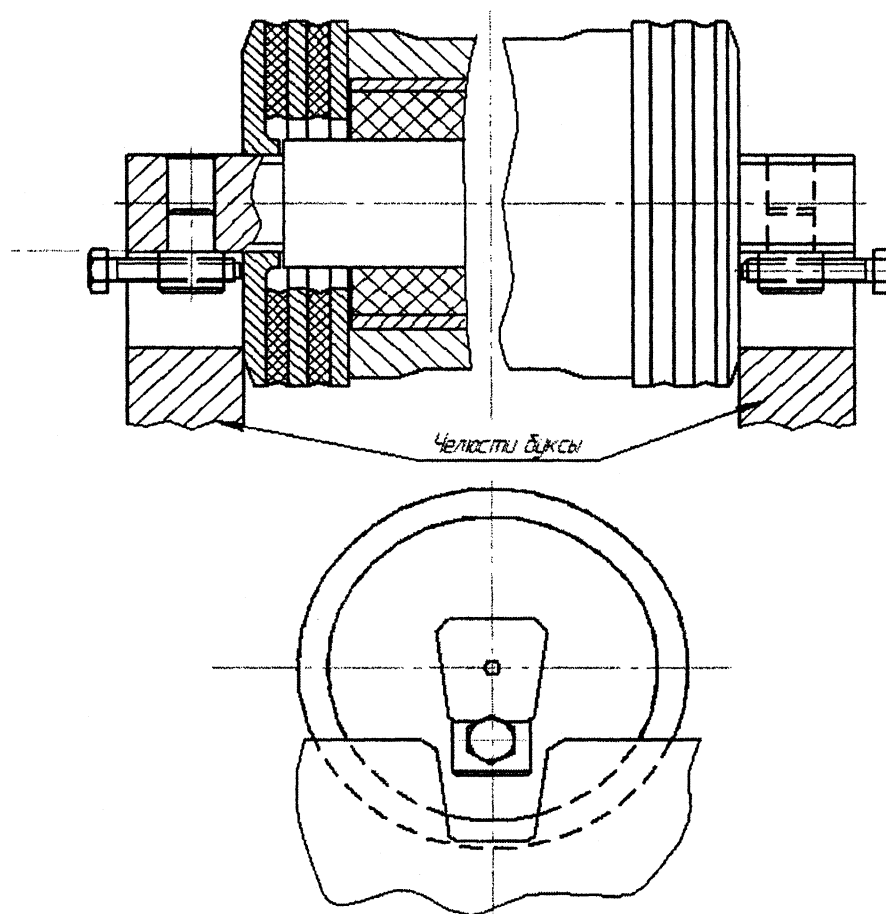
Установка поводка в челюсть буксы при помощи приспособления для предварительного поджатия торцевых шайб
